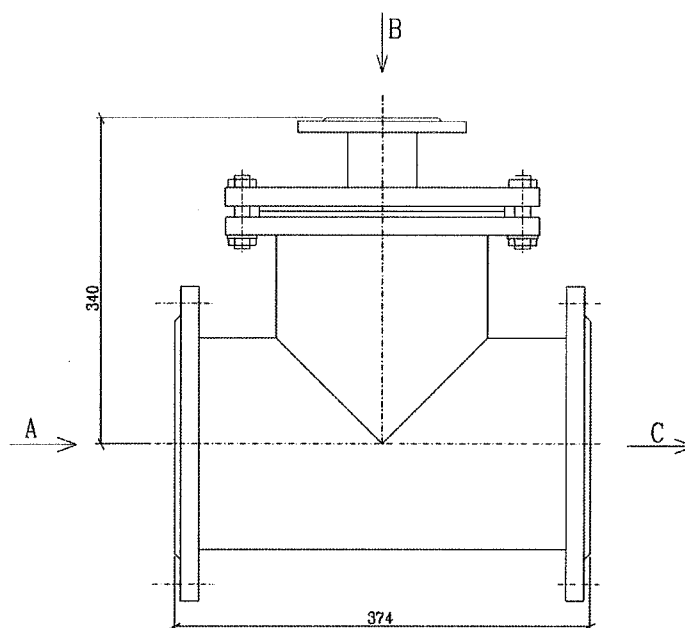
Габаритный чертеж смесителя для приготовления регенерационных растворов щелочи LDP20AM001
